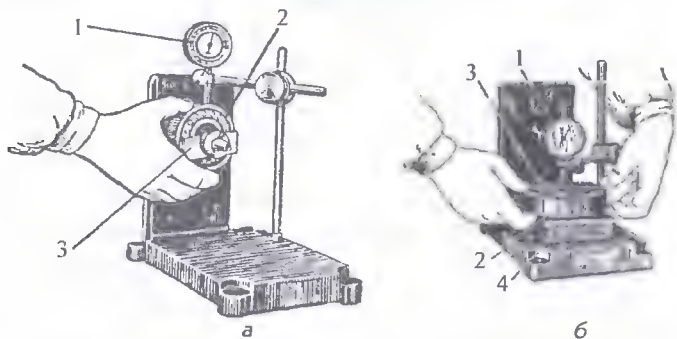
Измерение зазоров шарикового подшипника радиального (а), осевого (б): 1 — индикатор; 2 — шариковый подшипник; 3 — крепление; 4 — бруски
